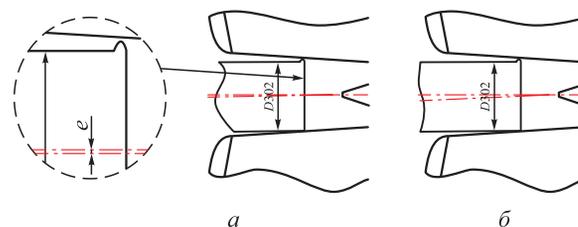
Отклонение заготовки от оси прокатки при первичном захвате: эксцентриситет осей заготовки и прокатки (а); угол наклона заготовки (б)
